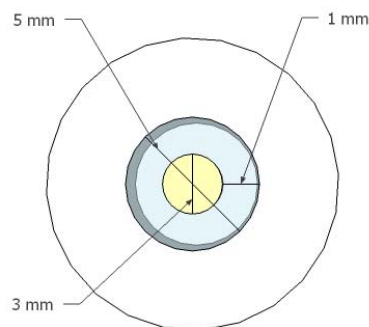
Rappresentazione schematica dell'holder con vista dall'alto.
